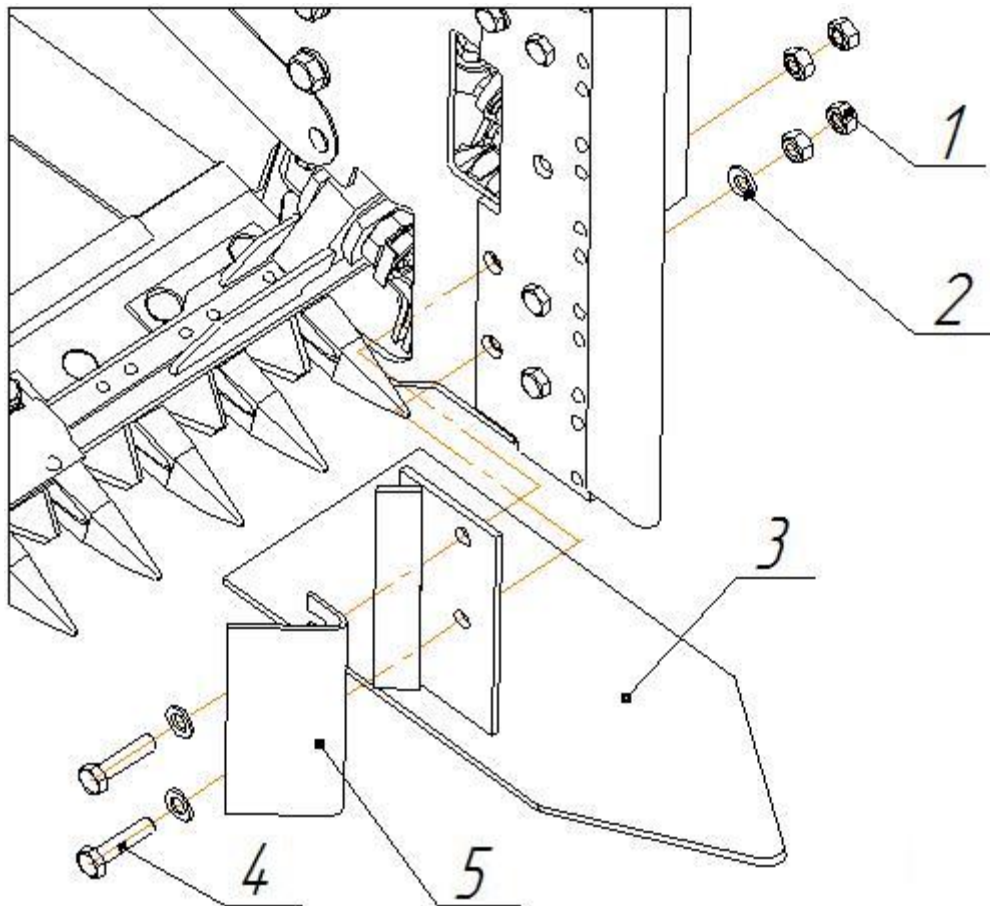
Крепление щитка ПРБЖ-00.030 к левой стороне приспособления и щитка ПРБЖ-00.030-01 к правой боковине приспособления.
